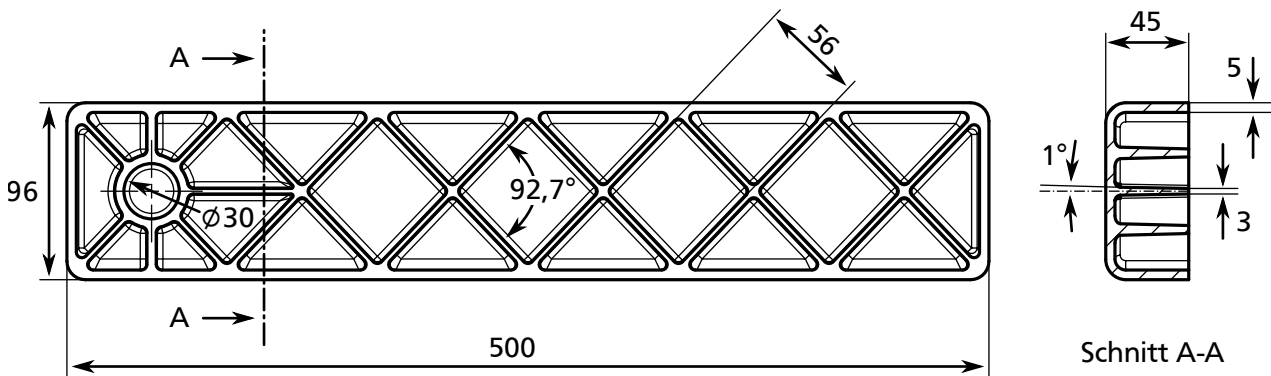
Geometrie des HLV-Trägers. Alle Maße in mm. Die Entformungsschräge der Rippen beträgt 1°. Die Gurte sind ohne Entformschräge ausgeführt, um parallele Schweißflächen sicherzustellen (vgl. Bild 3.9).
